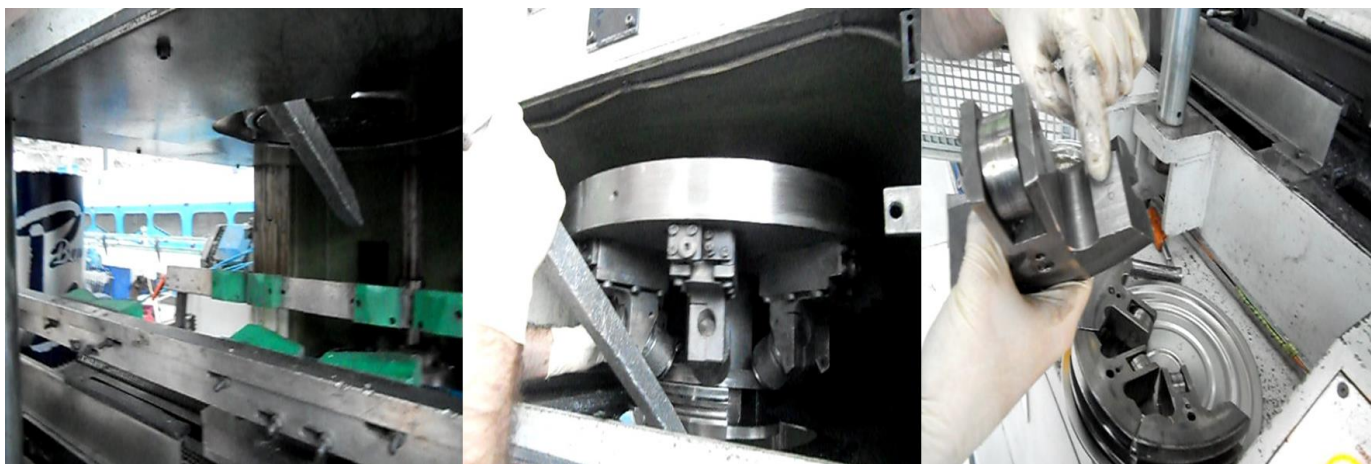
Ferramentas e chapa da máquina de rebordo e canal
